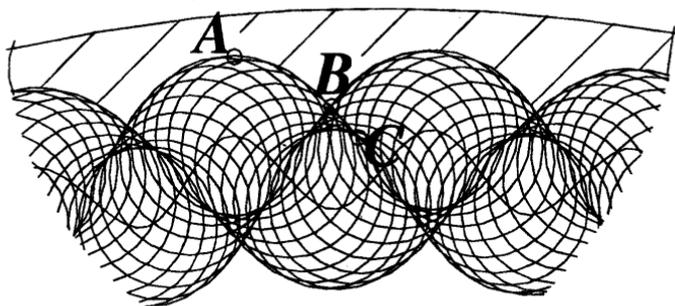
Фрагмент профиля кулачково-плунжерного зацепления с подрезанными вершинами
